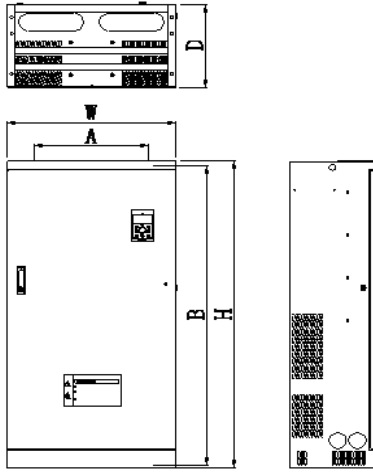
380V (4T) 160~400kW 变频器外型尺寸及安装尺寸示意图
